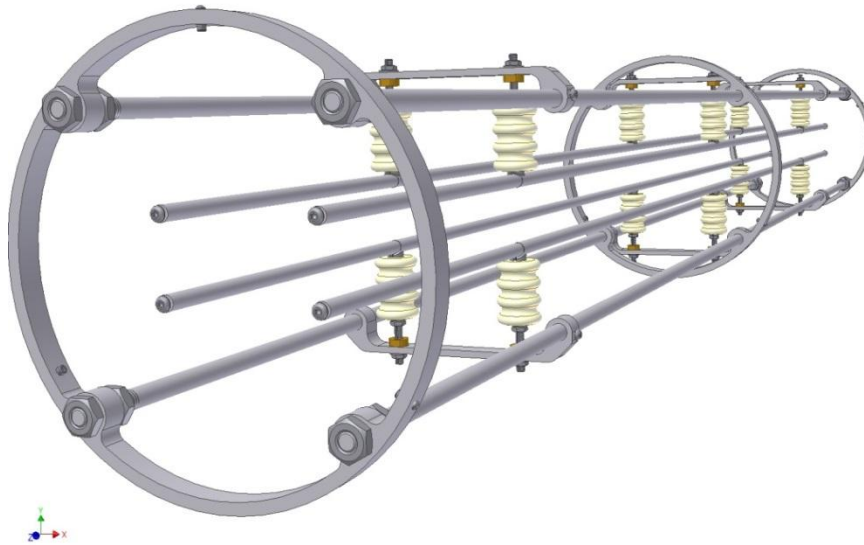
Вид ударного магнита с опорной конструкцией
